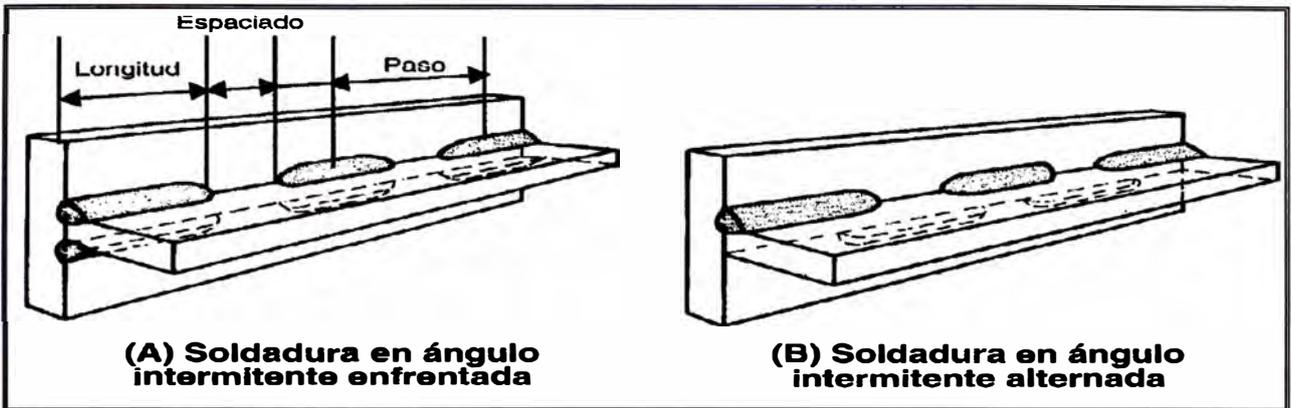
Soldaduras en ángulo Intermitente
